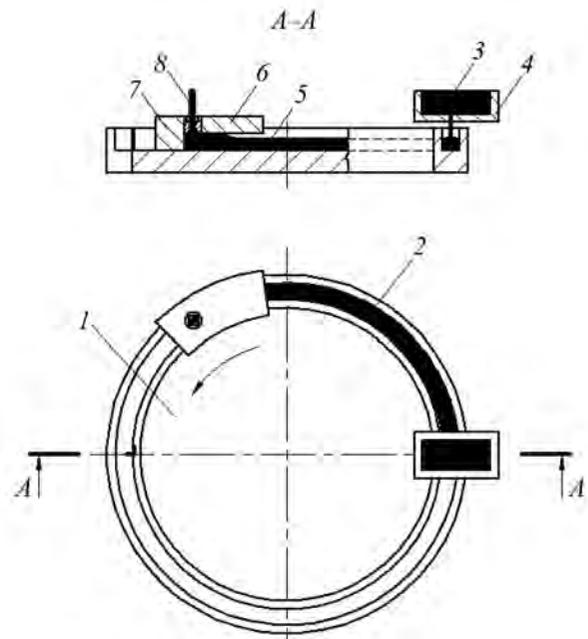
Схема установки непрерывного литья-прессования с вертикальной осью вращения колеса
